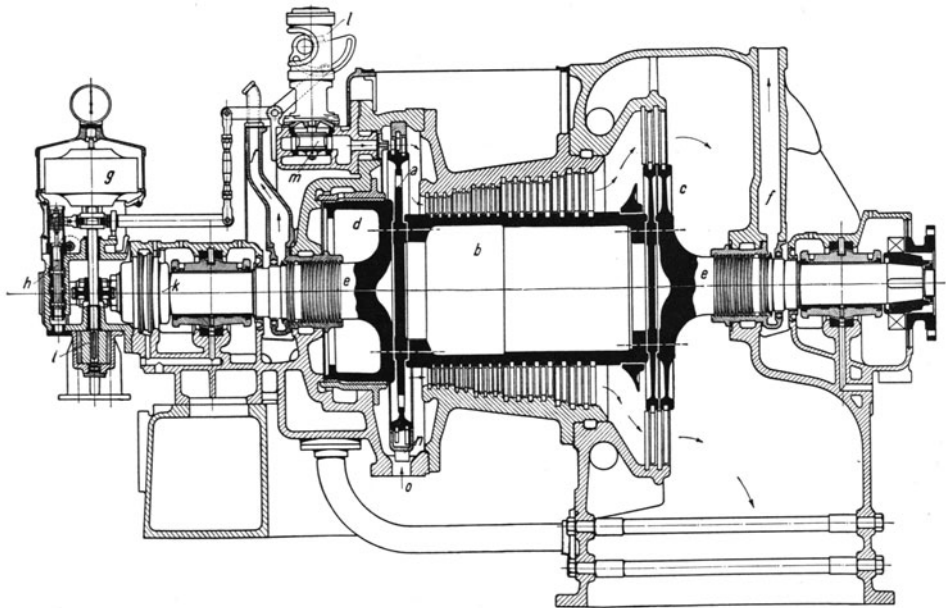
Dampfturbine der Maschinenfabrik Thyssen & Co.
